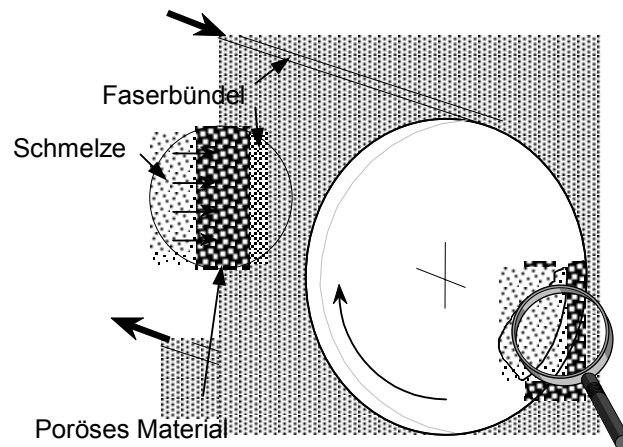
Faserbündel-Imprägnierung mittels Imprägnierrad [aus: 55]
